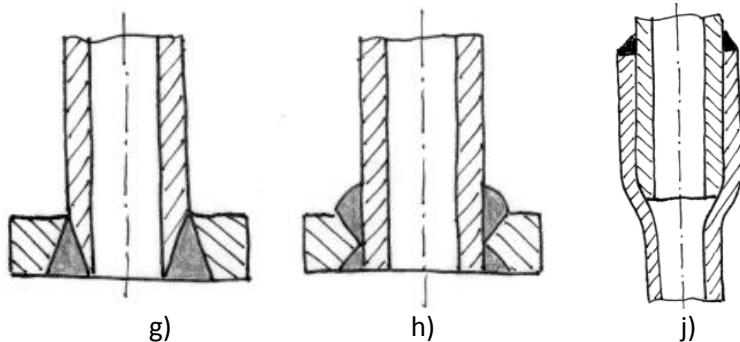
Rozdělení svarů podle styku spojovaných součástí
